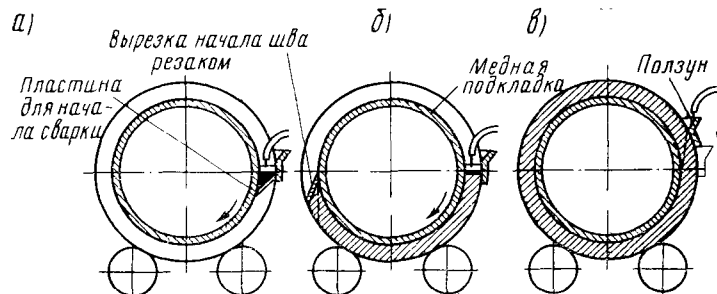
Схема электрошлаковой сварки кольцевых швов
